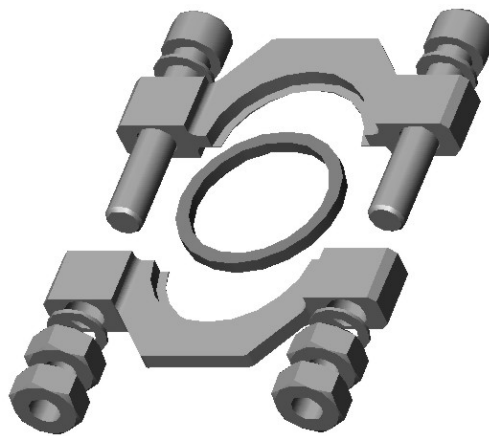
Vista explodida do dispositivo de compressão dos corpos-de-prova de fadiga de contato.
